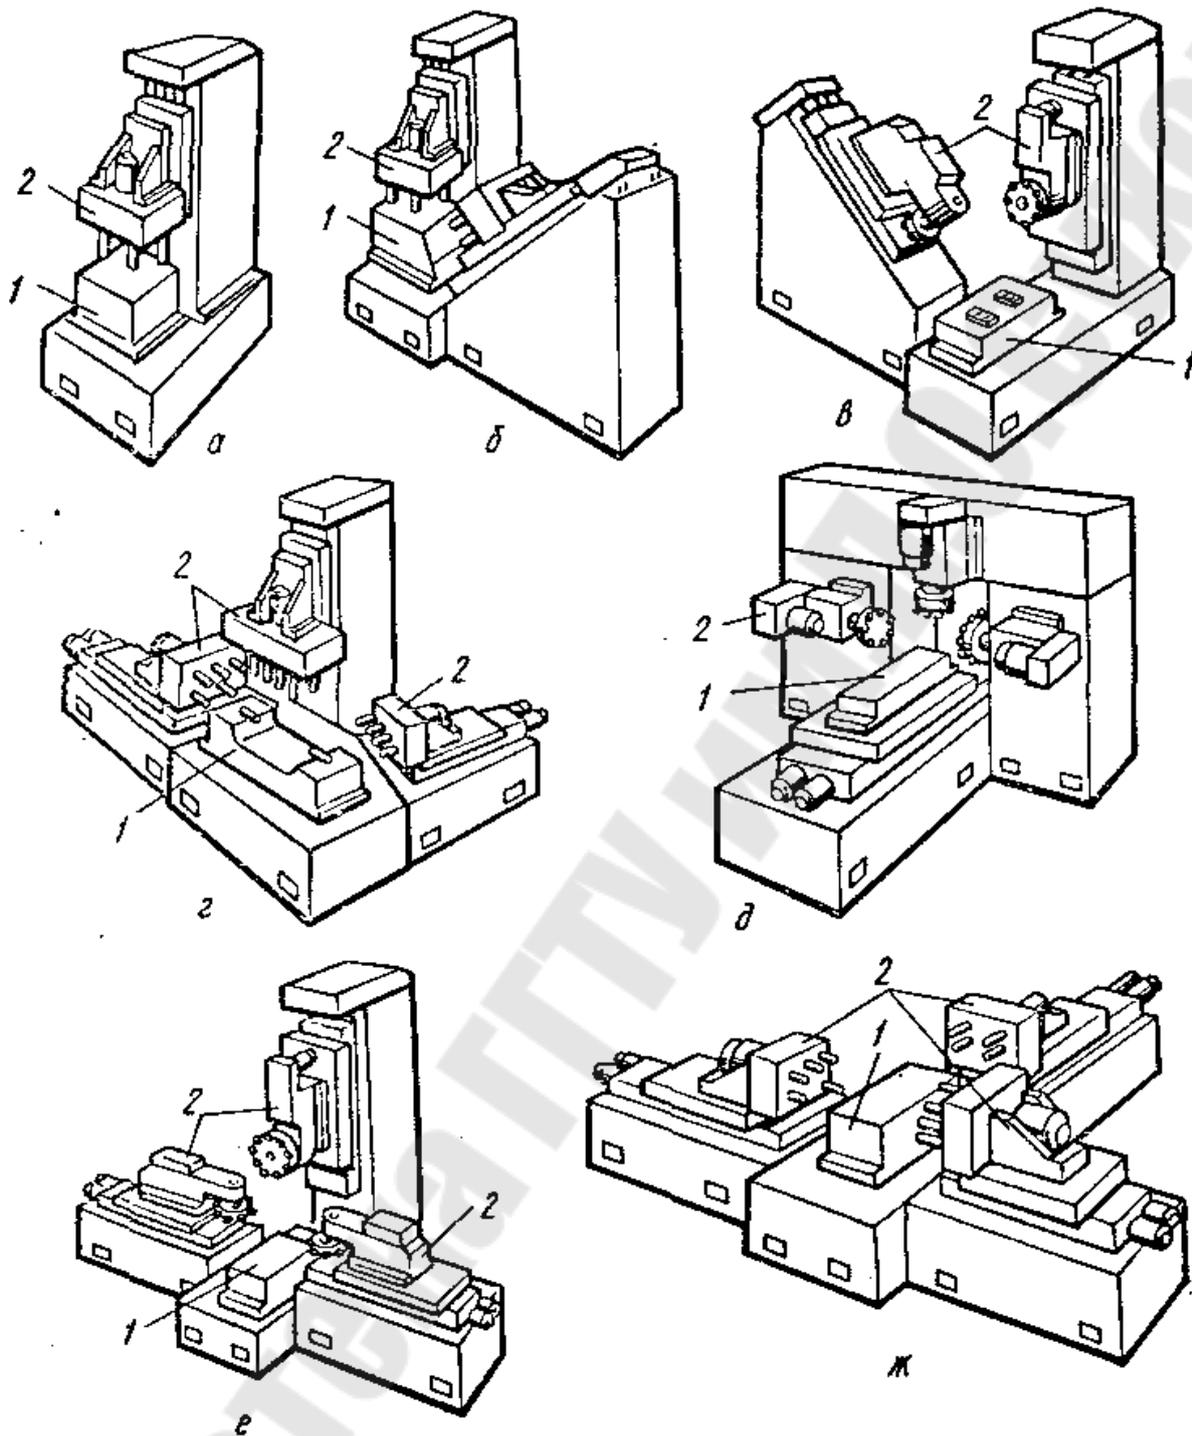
Типовые компоновки агрегатных станков со стационарным приспособлением
